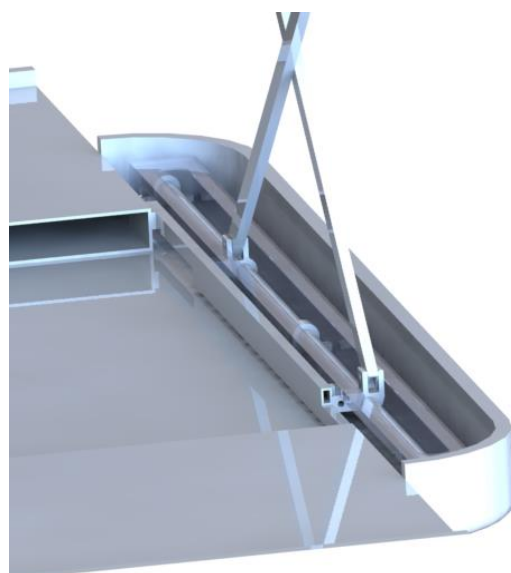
Vista detallada de las guías laterales en el sistema piñón-cremallera. (Fuente: Propia)
